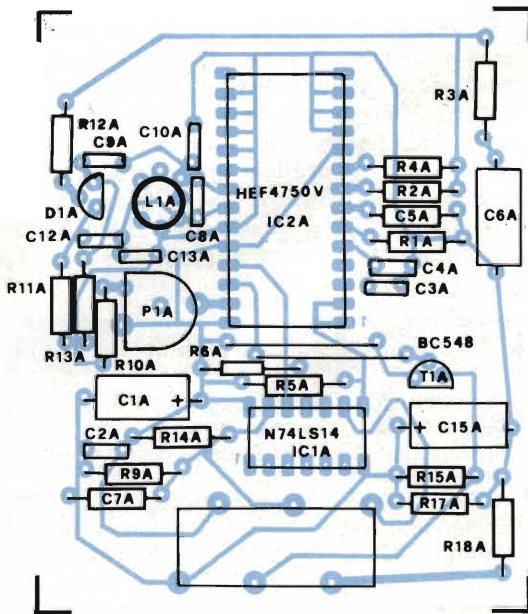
Disposizione dei componenti nello stampato di fig. 5.
